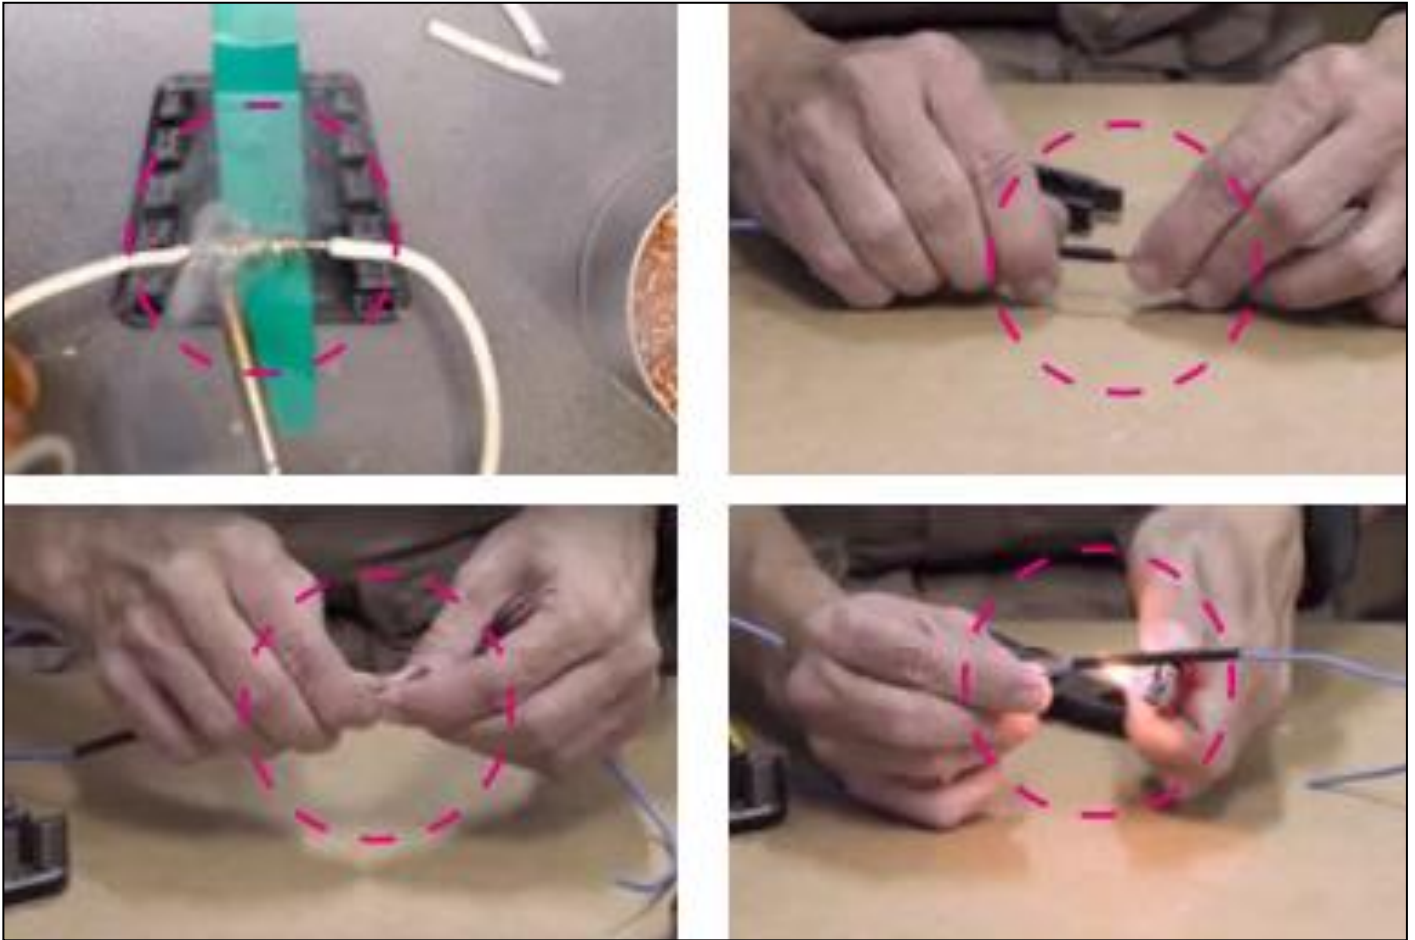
Instalación eléctrica y soldadura.
